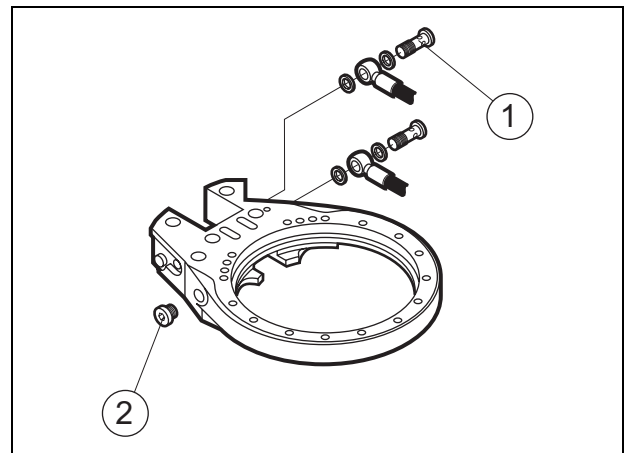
Soupape d'arrêt pour tendre la chaîne
